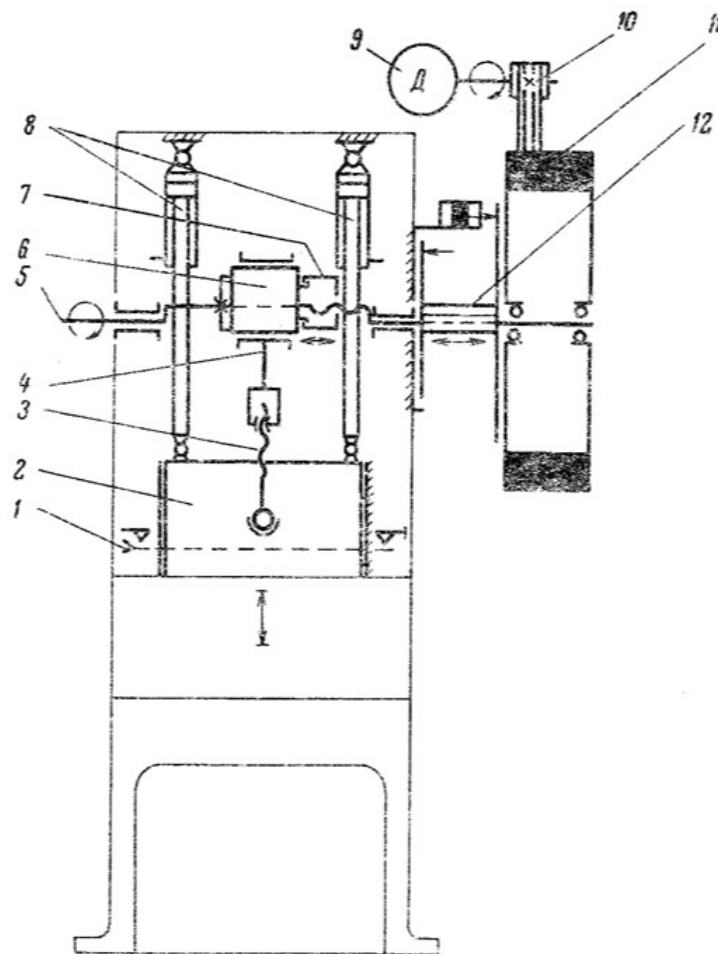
Кінематична схема одно-кривошипного верстату КД-2124
